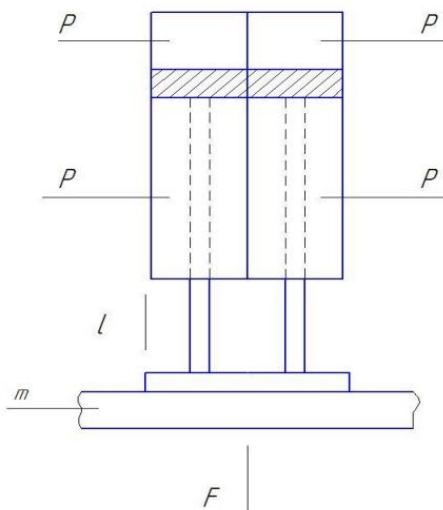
Кінематична загальна схема пневмопривода зварювання плівки
